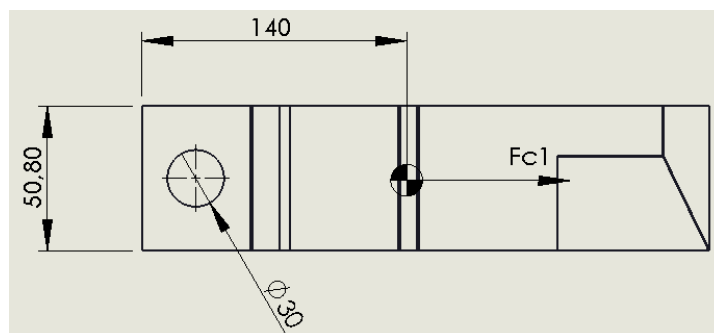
Dimensiones de la cuchilla oscilante, vista superior.
